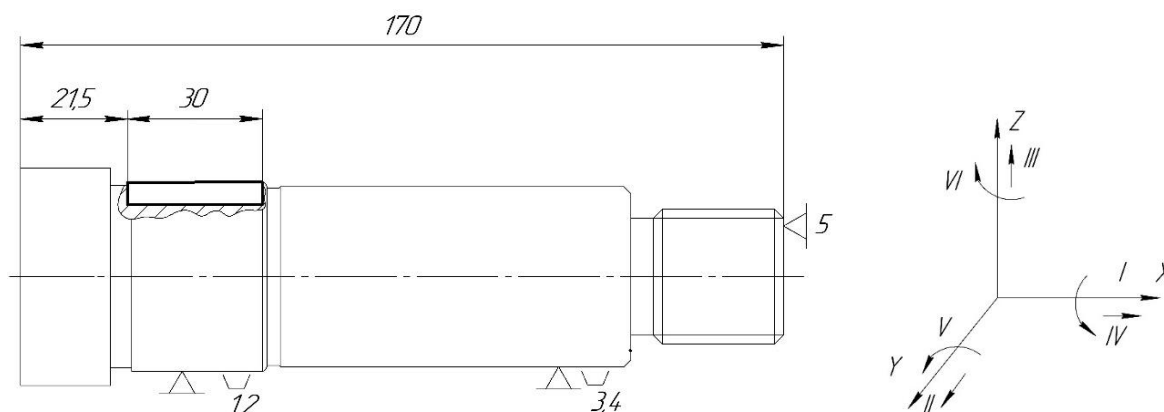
Схема базування та закріплення заготовки на операцію 030 Вертикально-фрезерну з ЧПК
